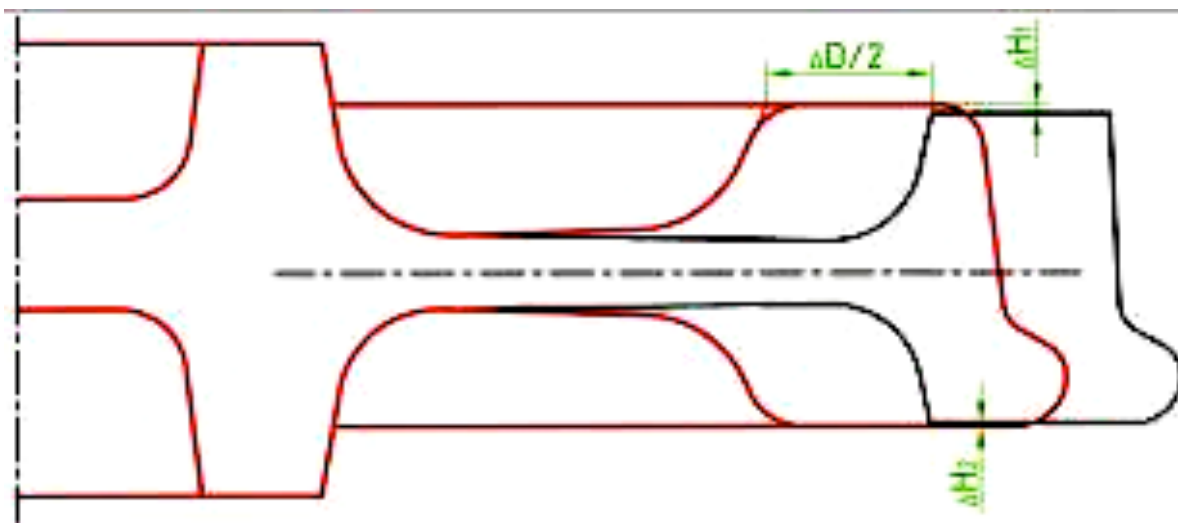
Форма штампованной поковки и прокатанной заготовки колеса
